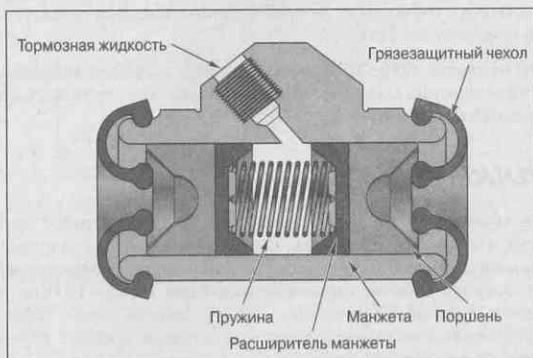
Конструкция рабочего тормозного цилиндра
